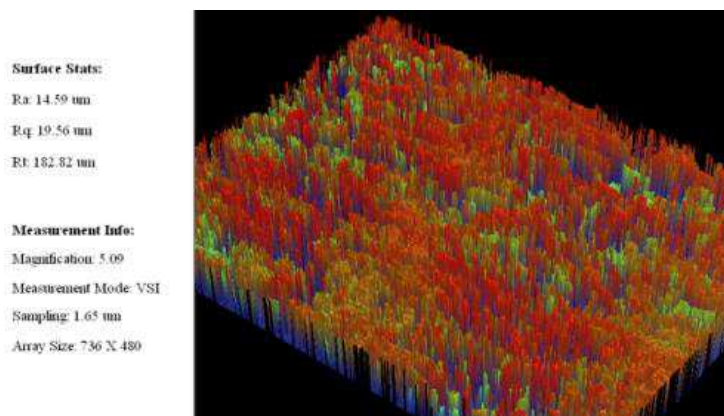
Exemple de relevé topographique d'une surface usinée par un outil revêtu de CrN après 110 m d'usinage
